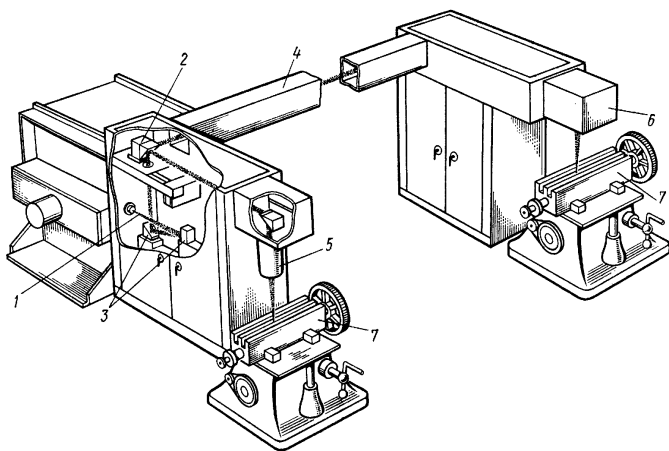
Схема мощной лазерной установки, разработанной для сварки и термообработки:
